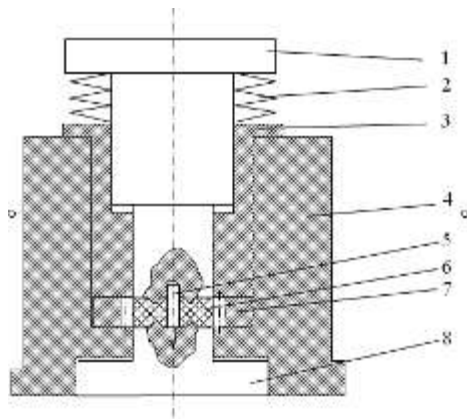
Прессформа для штамповки зубчатых колёс из термопластов в твёрдом состоянии: 1-пуасон верхний; 2-пружина тарельчатая; 3-стакан; 4-обойма; 5-знак; 6-изделие; 7- матрица; 8- пуасон нижний
